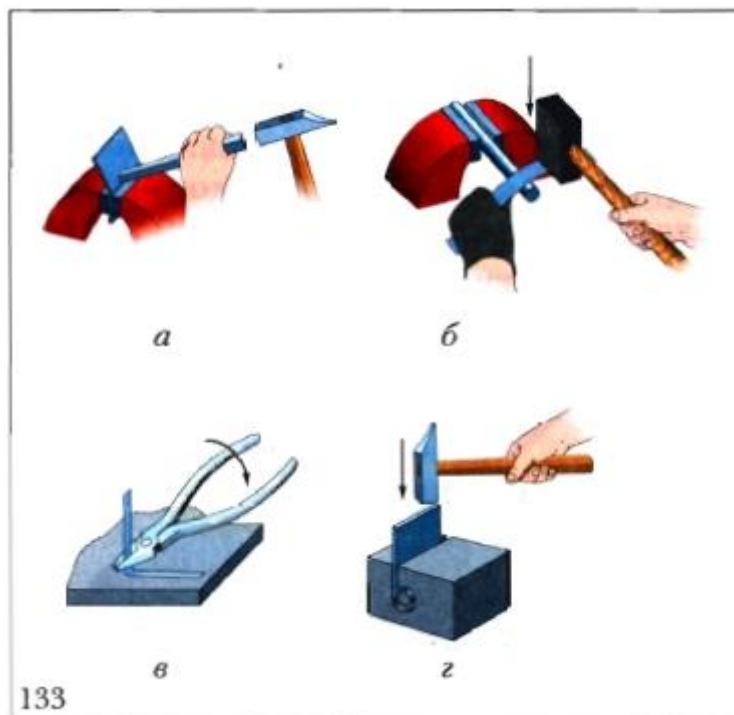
Гибка металлического листа: а — в тисках; б — на оправке; в — круглогубцами; г — в гибочном приспособлении
